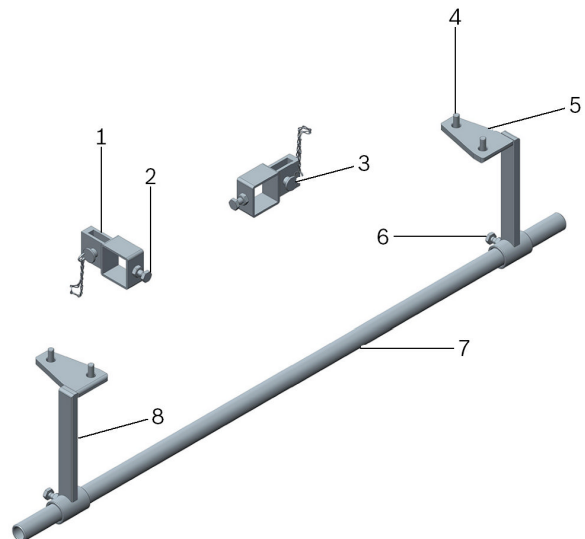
Вспомогательный комплект опорного приспособления для двигателя T40092
